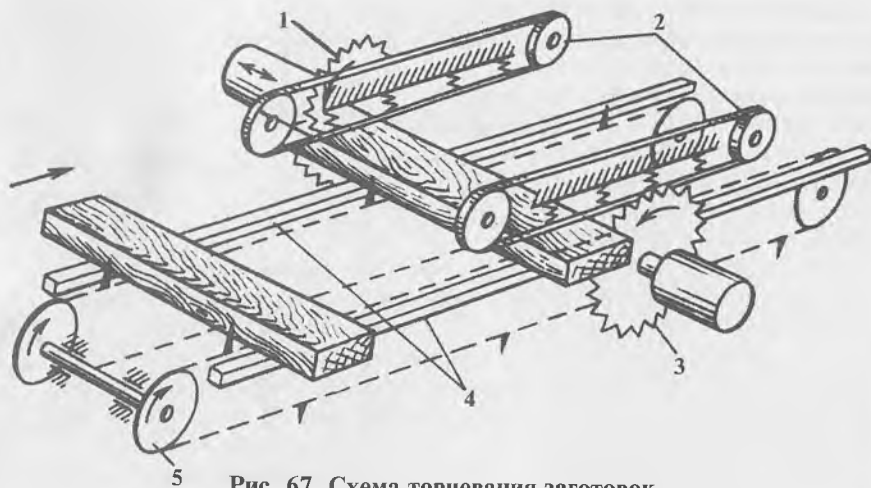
Схема торцевания заготовок на двухпильном концевальном станке:
